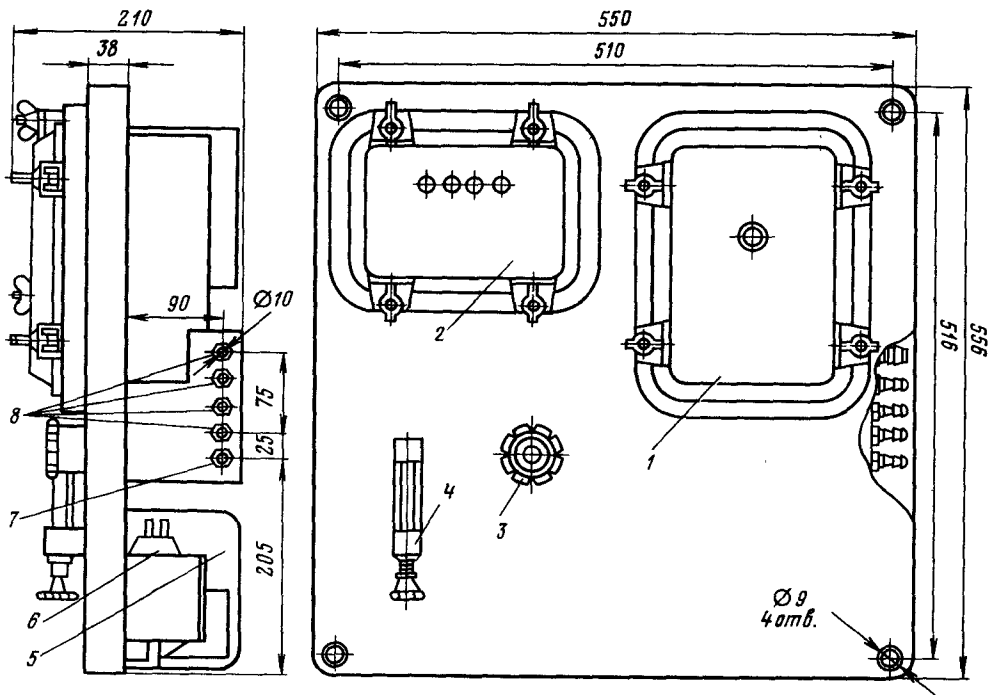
Габаритные и установочные размеры блока газоанализатора МН5122-1:
